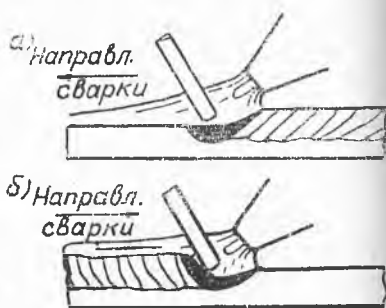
Левый (а) и правый (б) способы сварки.
